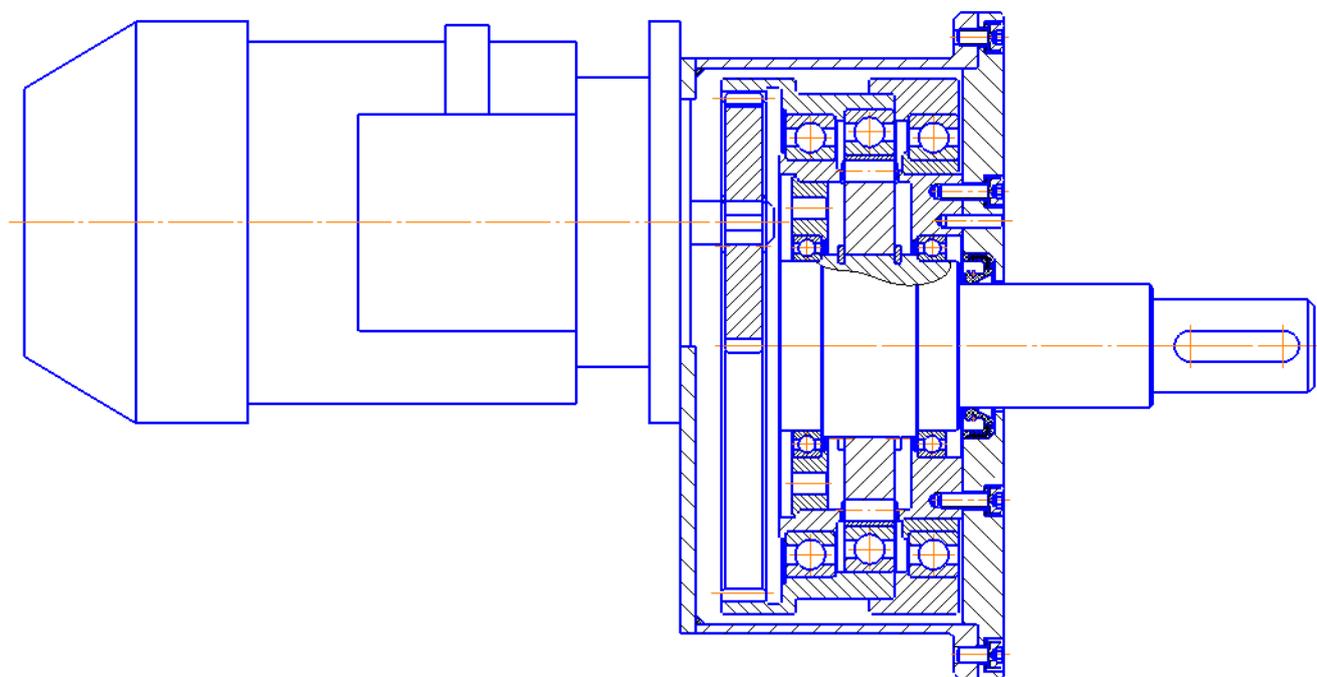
Схема привода волнового редуктора с внутренним зубчатым зацеплением
